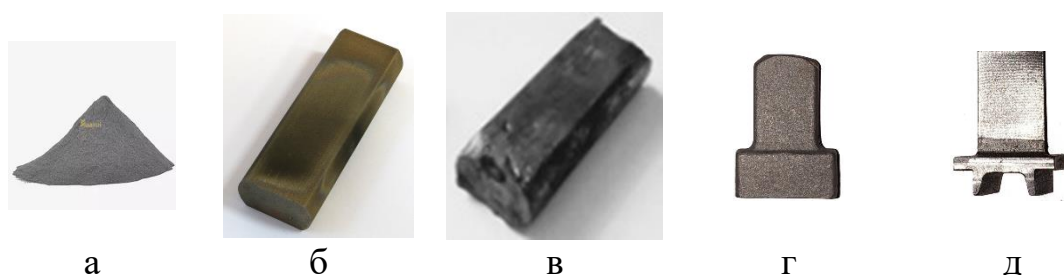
Лопатка ГТД на основних операціях процесу виготовлення: а – порошкова суміш; б – спечена заготовка; в – напівфабрикат (після гвинтової екструзії); г – заготовка лопатки (після термічної обробки); д – лопатка ГТД (після механічної обробки)
